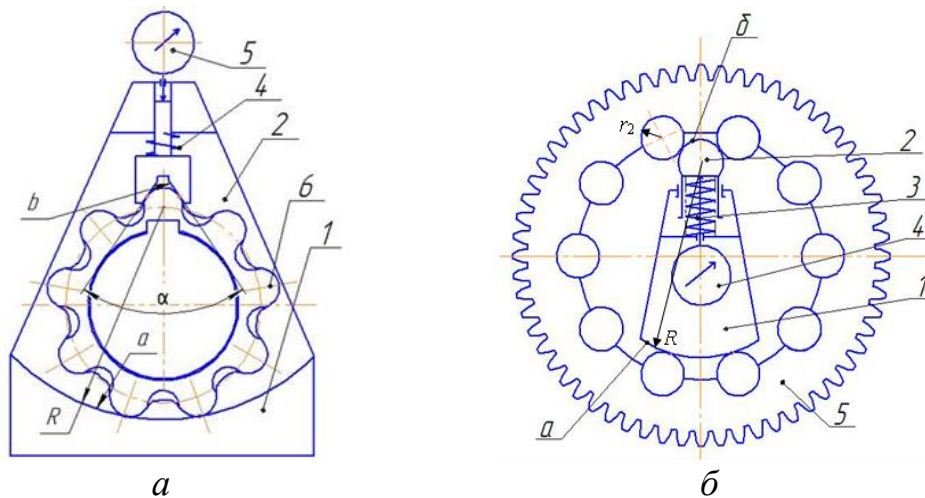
Схема пристроїв для контролю зубчастого контуру:
